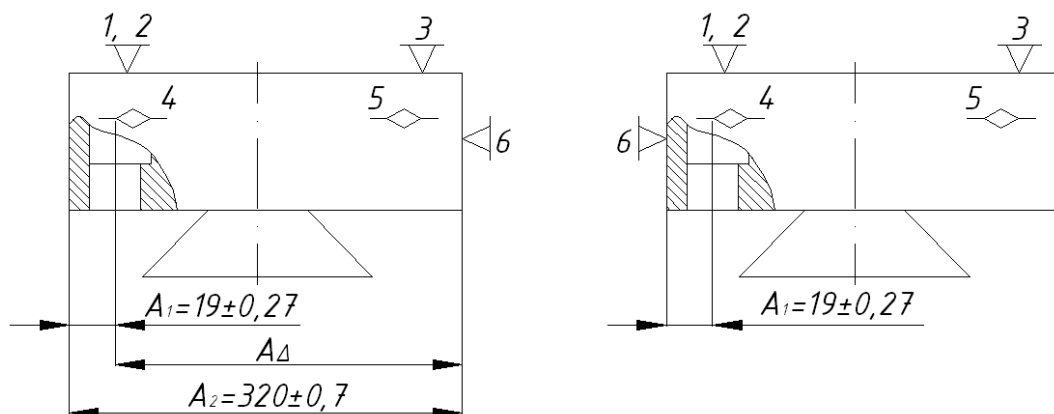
Теоретична схема базування при обробленні шпонкового паза 16
